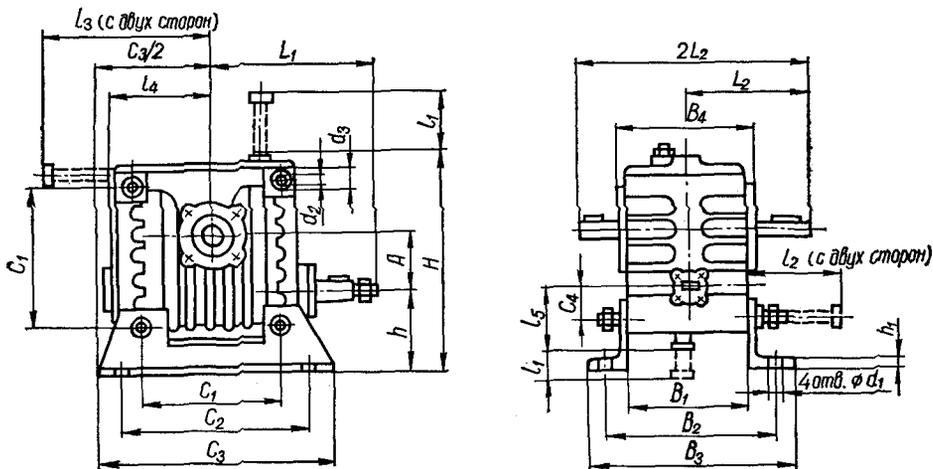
Основные и габаритные размеры редукторов РЧУ.
